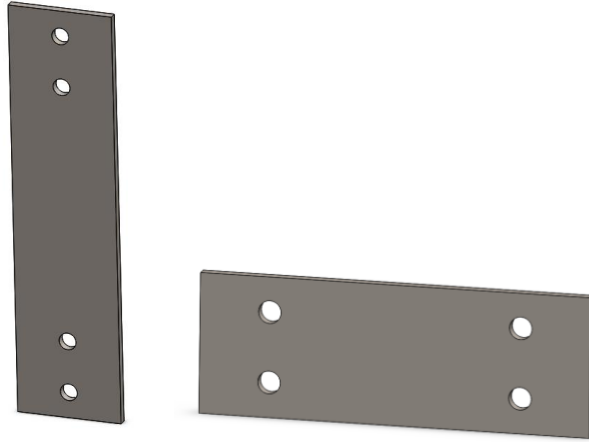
Modelo CAD del soporte de espalda horizontal
